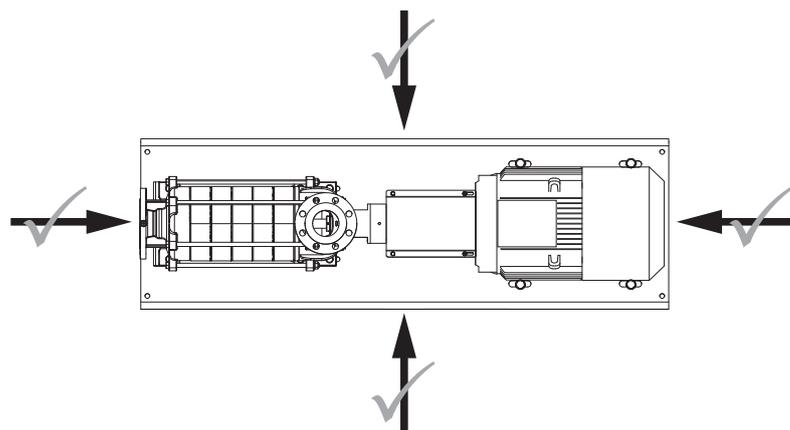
Pumpe mit Motor auf einer Grundplatte mit 650 mm Breite
